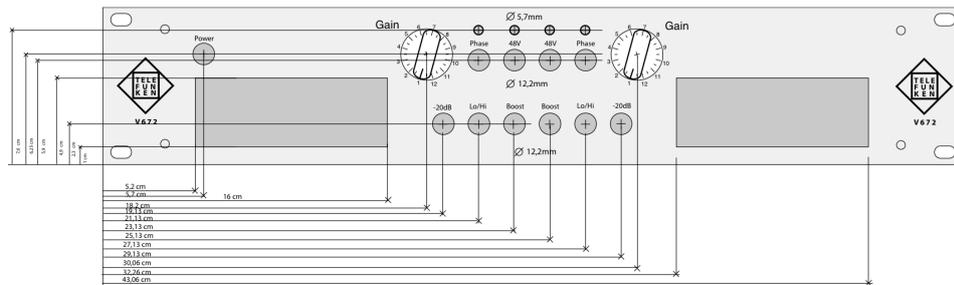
CAD-Konstruktionszeichnung aus Adobe Illustrator
